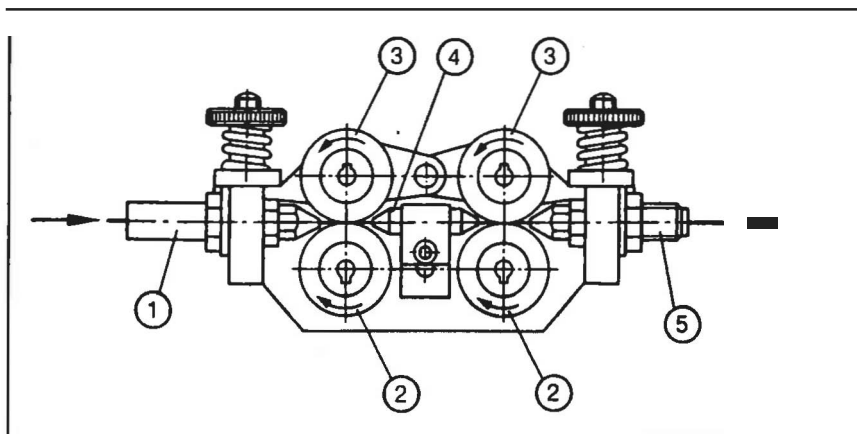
ALIMENTADOR DE ALAMBRE DE CUATRO RODILLOS
